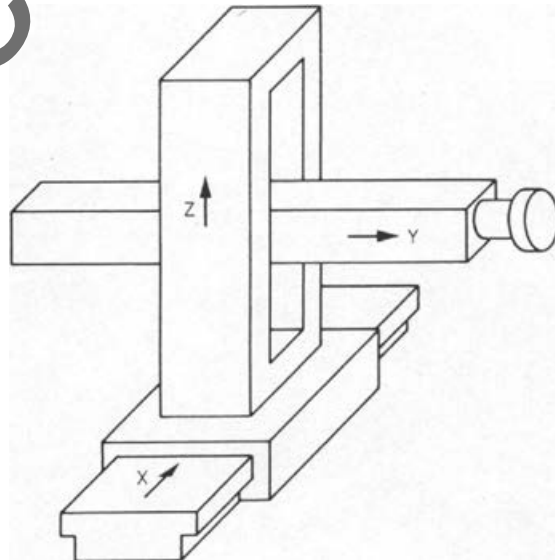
Beispiel eines Industrieroboters zum Schutzgasschweißen mit drei linearen Hauptachsen.
